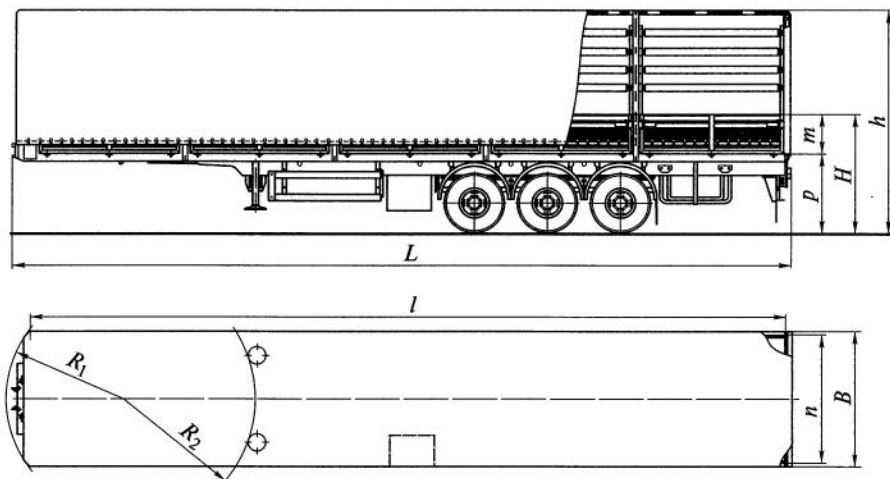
Условные обозначения основных размеров полуприцепа
